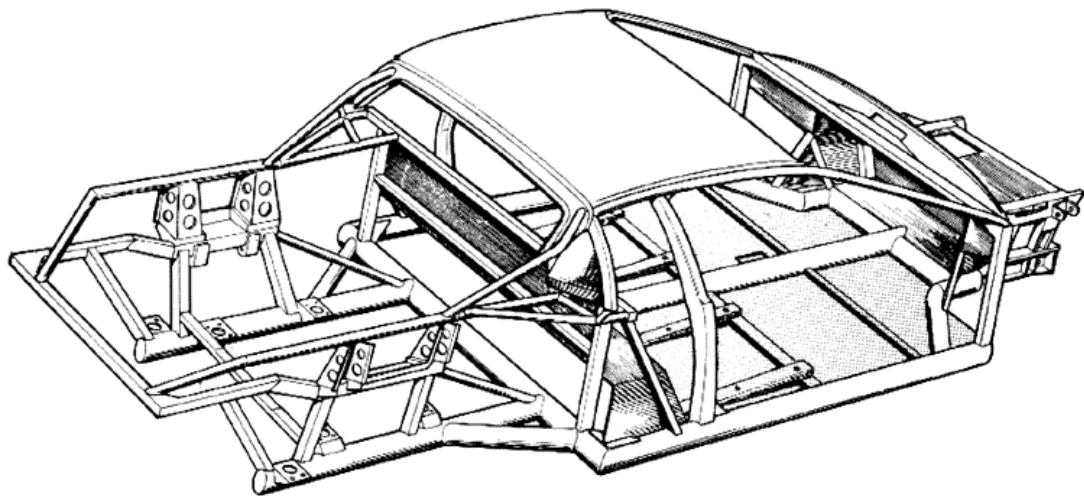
Telaio tubolare in acciaio (Ferrari Testarossa, 1984)
